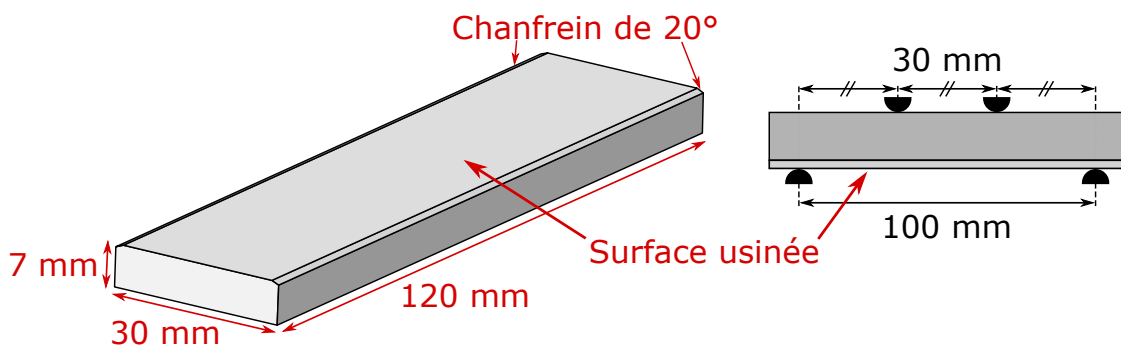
Dimensions des éprouvettes de fatigue.
